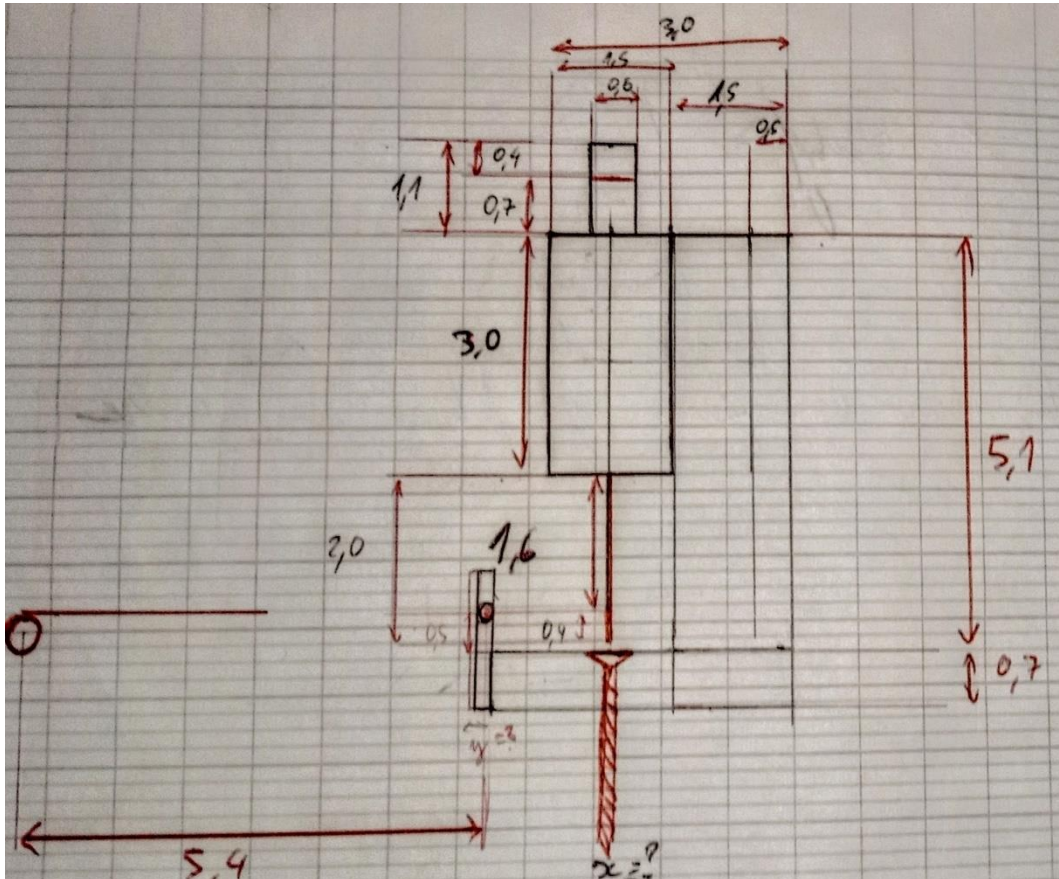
Croquis de dimensions du dispositif, vue de côté
